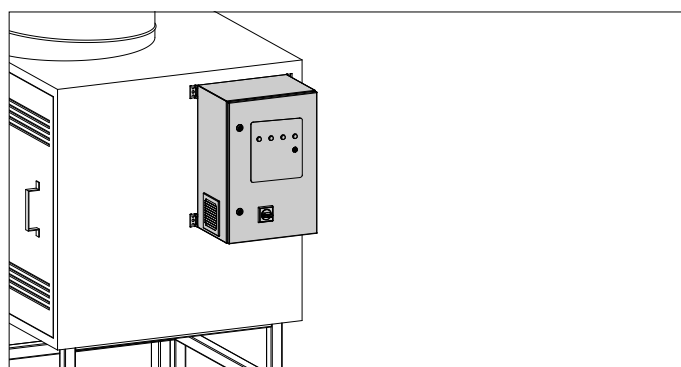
Montage du Panel sur le boîtier de ventilateur
